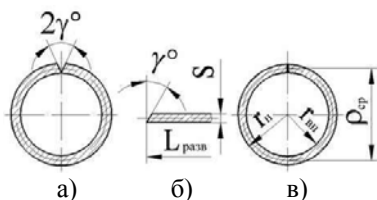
Форма поперечного сечения свертной втулки: а) V-образный стык, б) фаска на торцах заготовки, в) плотный стык замка
